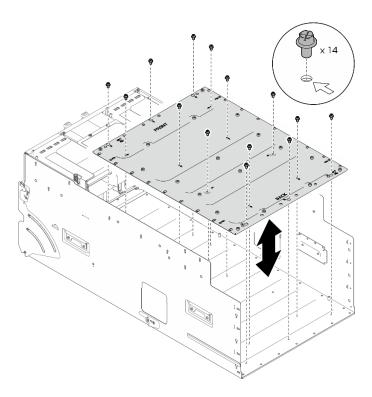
Entfernen der GPU-Komplex-Adapterplatte
